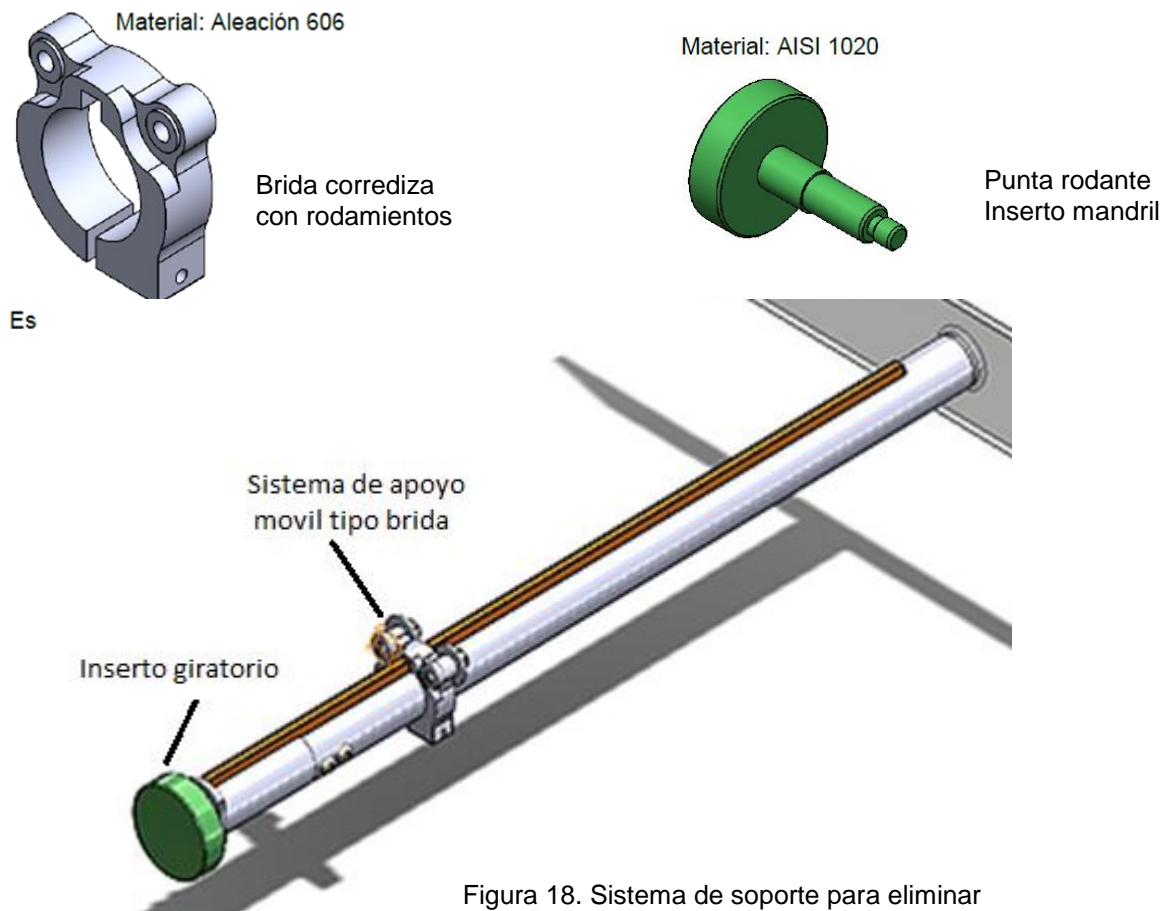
Sistema de soporte para eliminar fricción durante la soldadura orbital.
